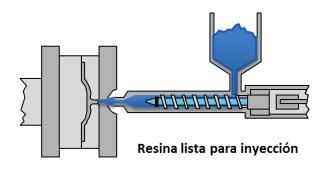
Esquema moldeo por inyección. Fuente: google.com
